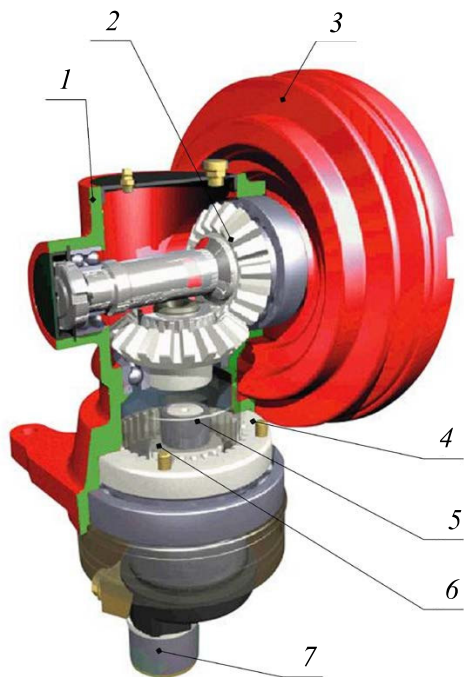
Планетарный механизм: 1 – корпус; 2 – коническая передача; 3 – приводной шкив; 4 – коронная шестерня; 5 – водило; 6 – сателлит; 7 – поводок
